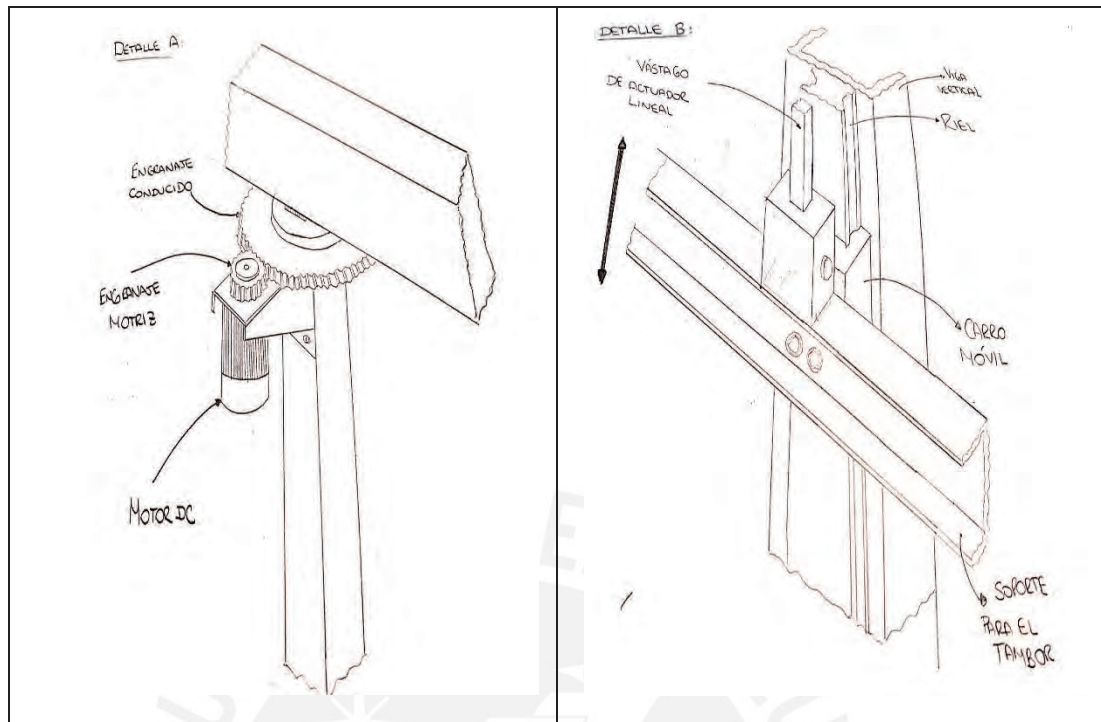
Detalles de la solución N° 03. a) Detalle A del sistema. b) Detalle B del sistema.
